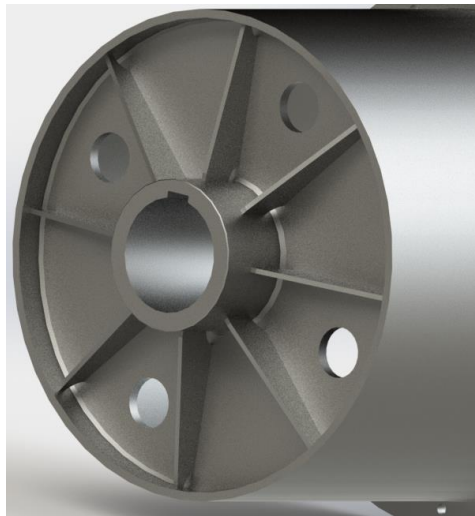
Soldadura do tubo onde será maquinado o cubo do veio do redutor planetário ao postigo exterior
